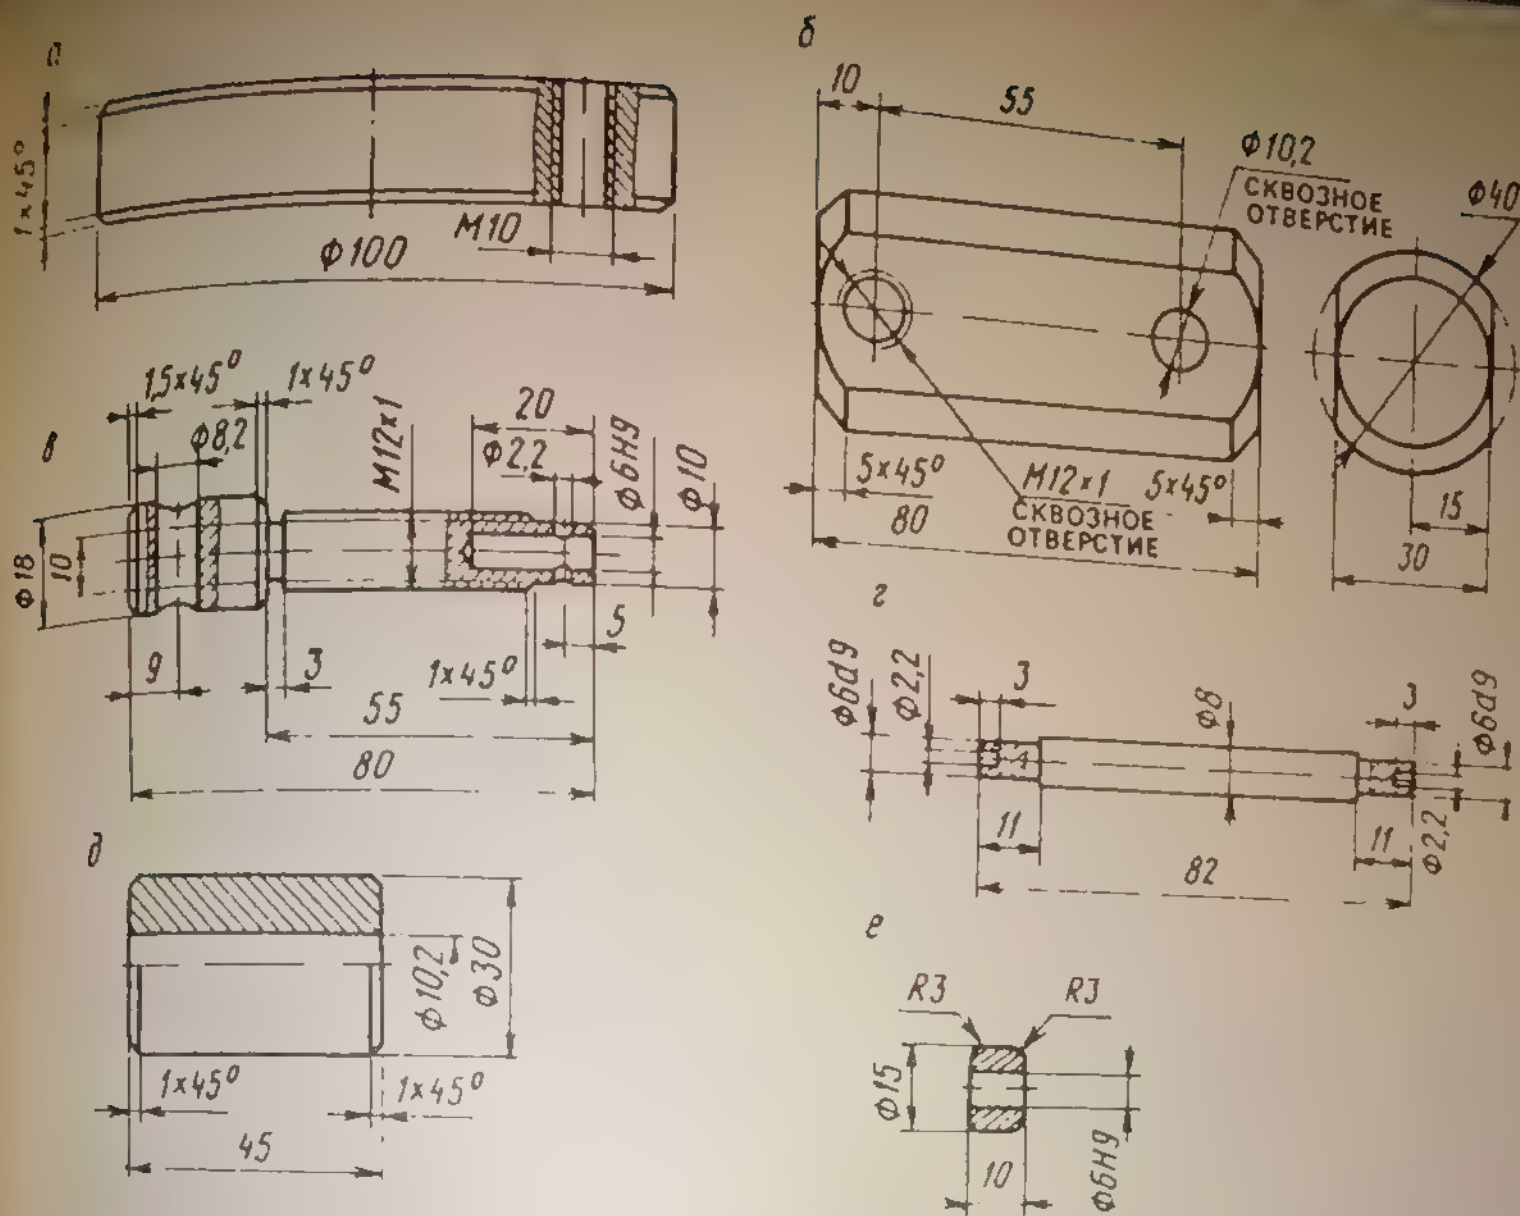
Основные детали корпуса приспособления для вырезания уплотняющих прокладок и уплотнительных колец
